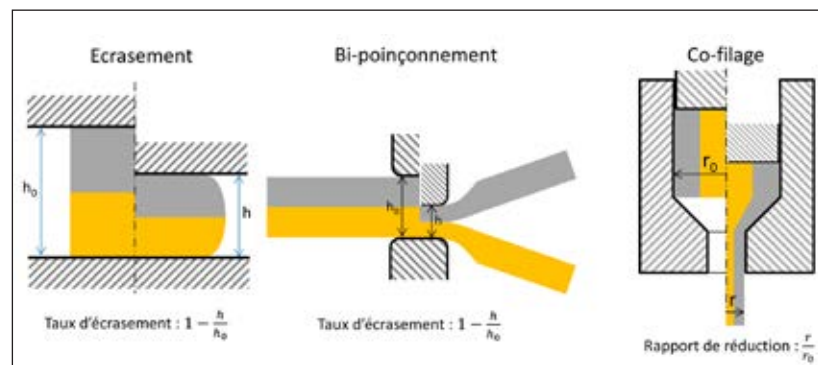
principe des essais de caractérisation de la co-forgeabilité d'un acier C55 sur un acier 25CrMo4
